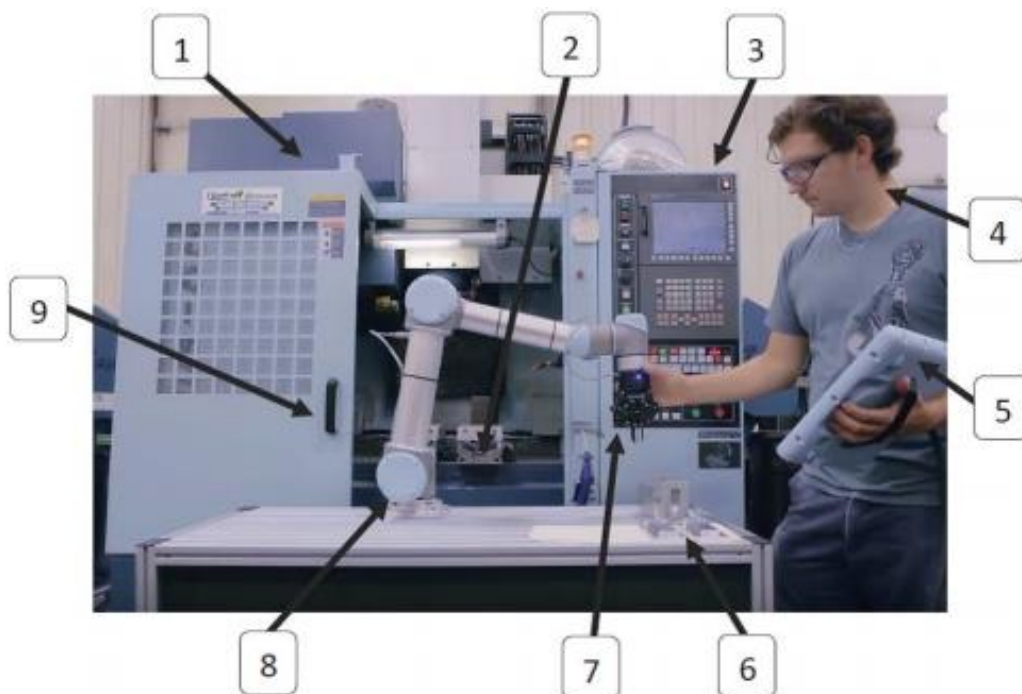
Strojní zařízení pro výměnu obrobku [5]
